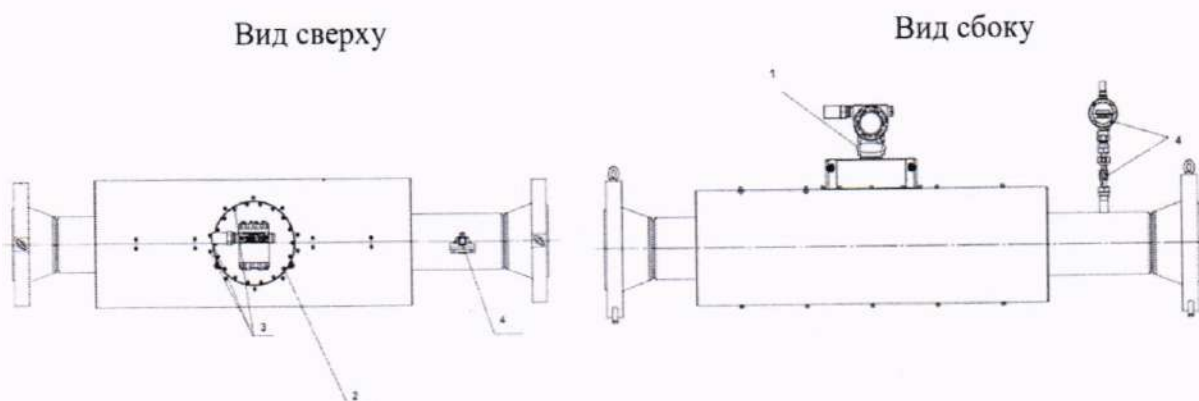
Корпус круглого сечения с защитным кожухом
